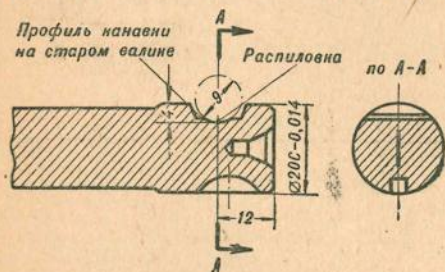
Эскиз распиловки старого валика привода электрогенератора под цилиндрический болт (дет. 309-30)
